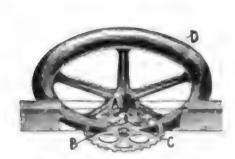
"Fixator"-Steuerrad. A = Spiral'eder, B = Welle, C = Kettenrad, D = Handrad.
